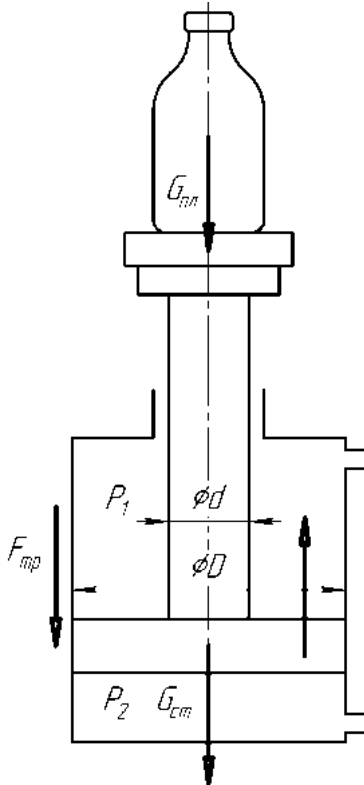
Розрахункова схема пневматичного підйомного столика
